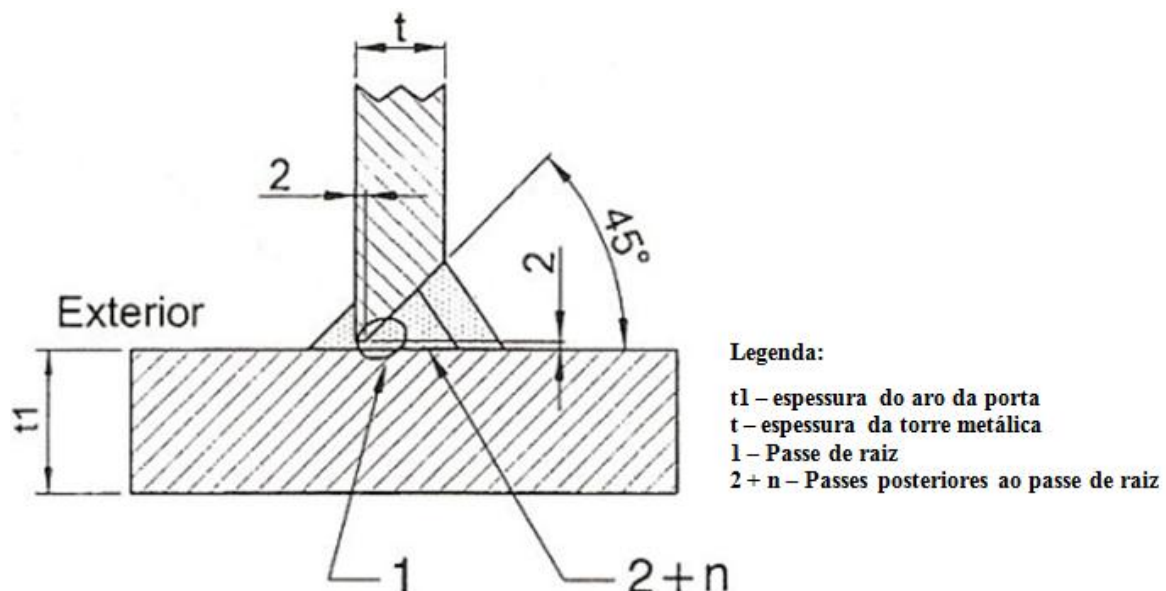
Junta de soldadura na união entre o aro da porta e a torre eólica [18]
